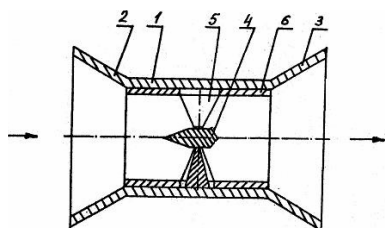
Пристрій з малим нерухомим кавітатором [21]: 1 – циліндричний трубопровід; 2 – патрубок підводу; 3 – патрубок відводу; 4 – ступиця; 5 – кавітатори; 6 – втулка
